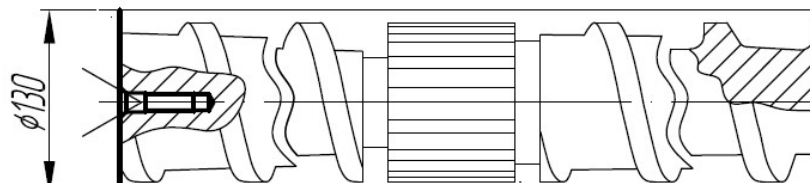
Схема базування заготовки на завершальних операціях
